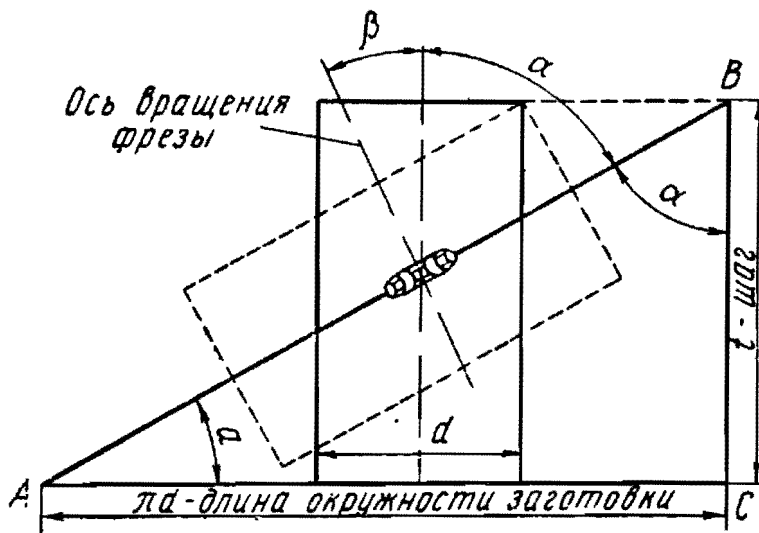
Схема установки стола станка с заготовкой винтового колеса
